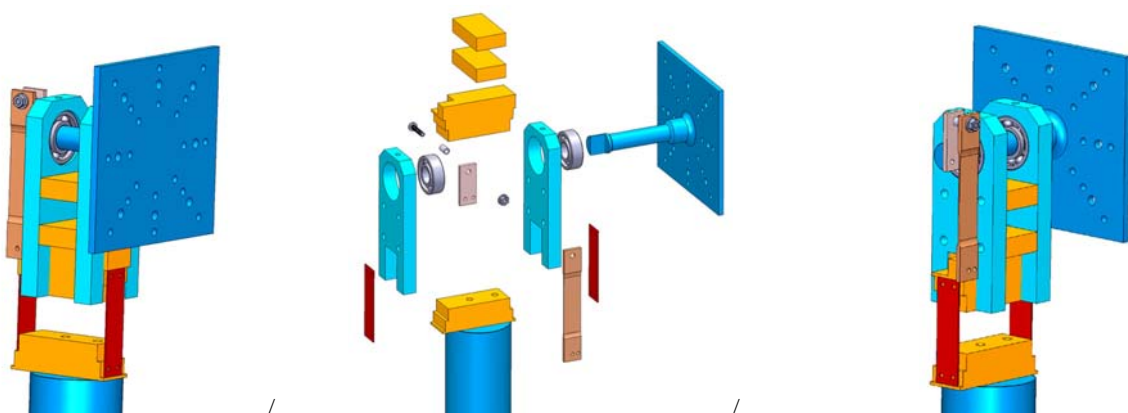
Cabeça da montagem: (a) vista frontal (b) Vista explodida e (C) Vista traseira.
